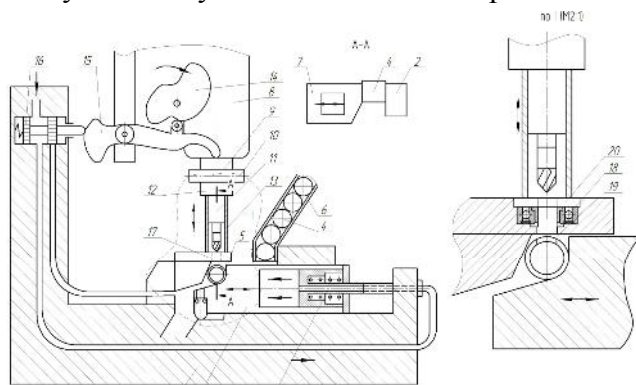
Пневматичний автоматизований пристрій для свердління і нарізання різи в трубчастих заготовках
